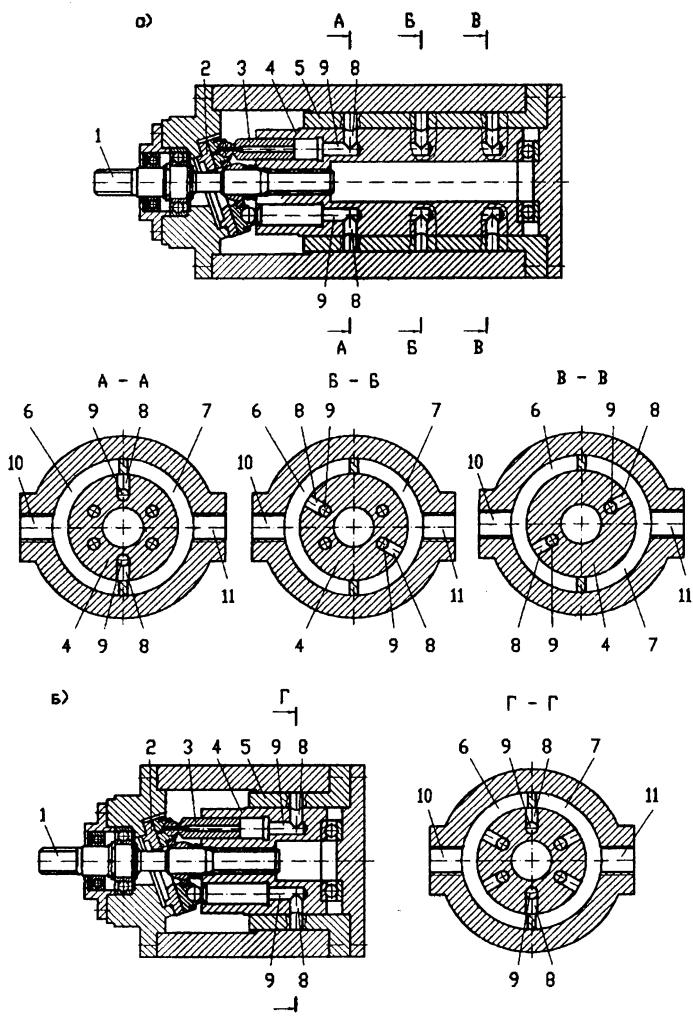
Аксиально-поршневая гидромашина: 1 – ведущий вал; 2 – наклонная шайба; 3 – поршень; 4 – блок цилиндров; 5 – подшипник скольжения; 6, 7 – полукольцевые пазы; 8, 9 – каналы блока цилиндров; 10, 11 – каналы корпуса гидромашины
